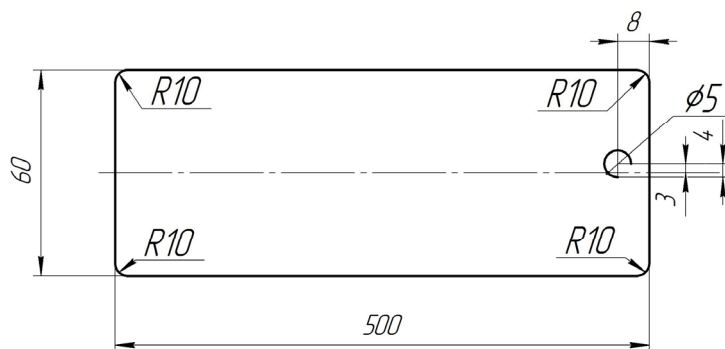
Приспособление для восстановления полок тетивы лестницы
